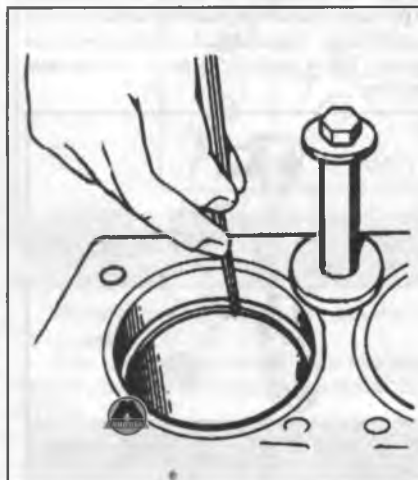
Подбор поршневых колец по цилиндру (проверка бокового зазора в замке кольца).
